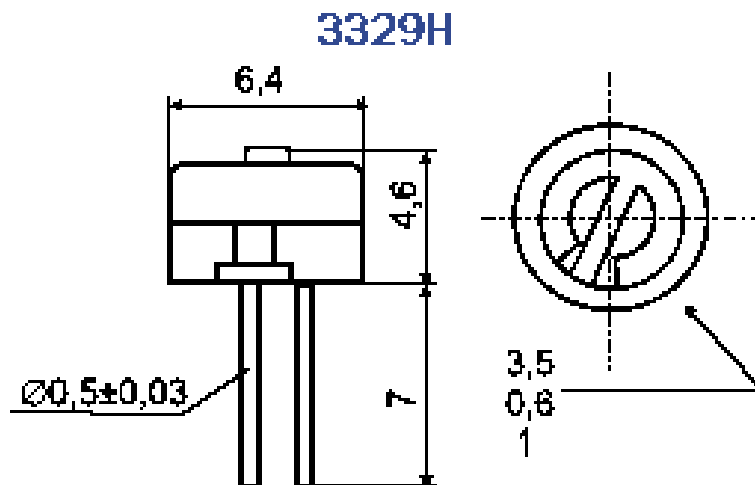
Габаритні розміри резистора підстроювального
